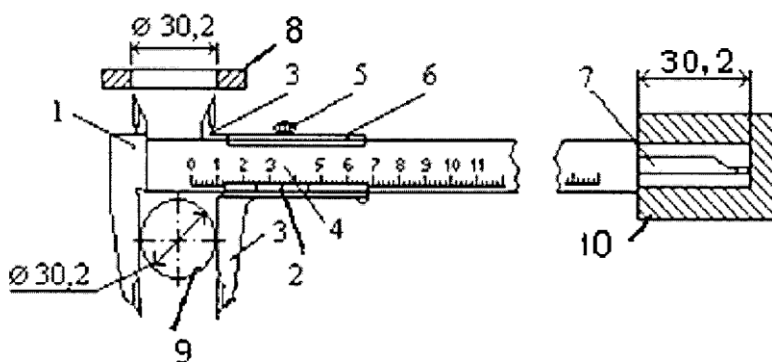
Измерение размеров детали с помощью штангенциркуля
